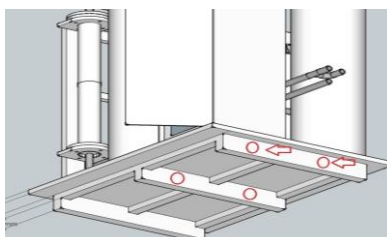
Pormenor da entrada dos garfos do empilhador nas vigas do suporte
